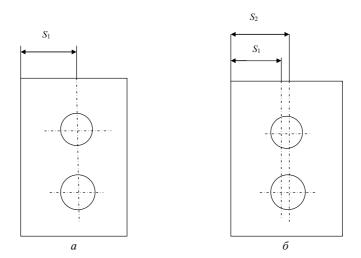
a – размеры на чертеже детали; δ – размеры на схеме обработки
